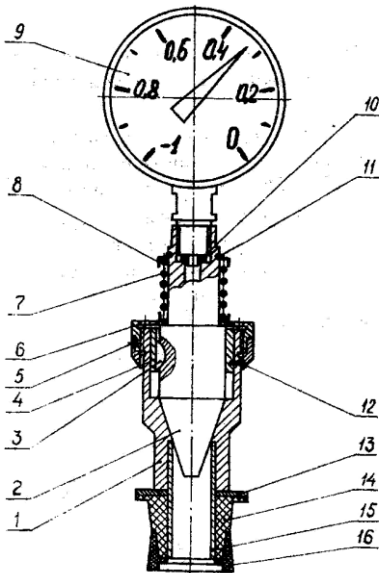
Індикатор продуктивності вакуумних насосів КІ-4840М: 1 - корпус; 2 - шпindelь; 3 - шпонка; 4 - втулка; 5 - штифт; 6 - барабан; 7 - пружина; 8 - кільце; 9 - вакуумметр; 10 - прокладка; 11 - кільце запірний; 12 - штифт; 13 - шайба; 14 - муфта; 15 - втулка; 16 - муфта
